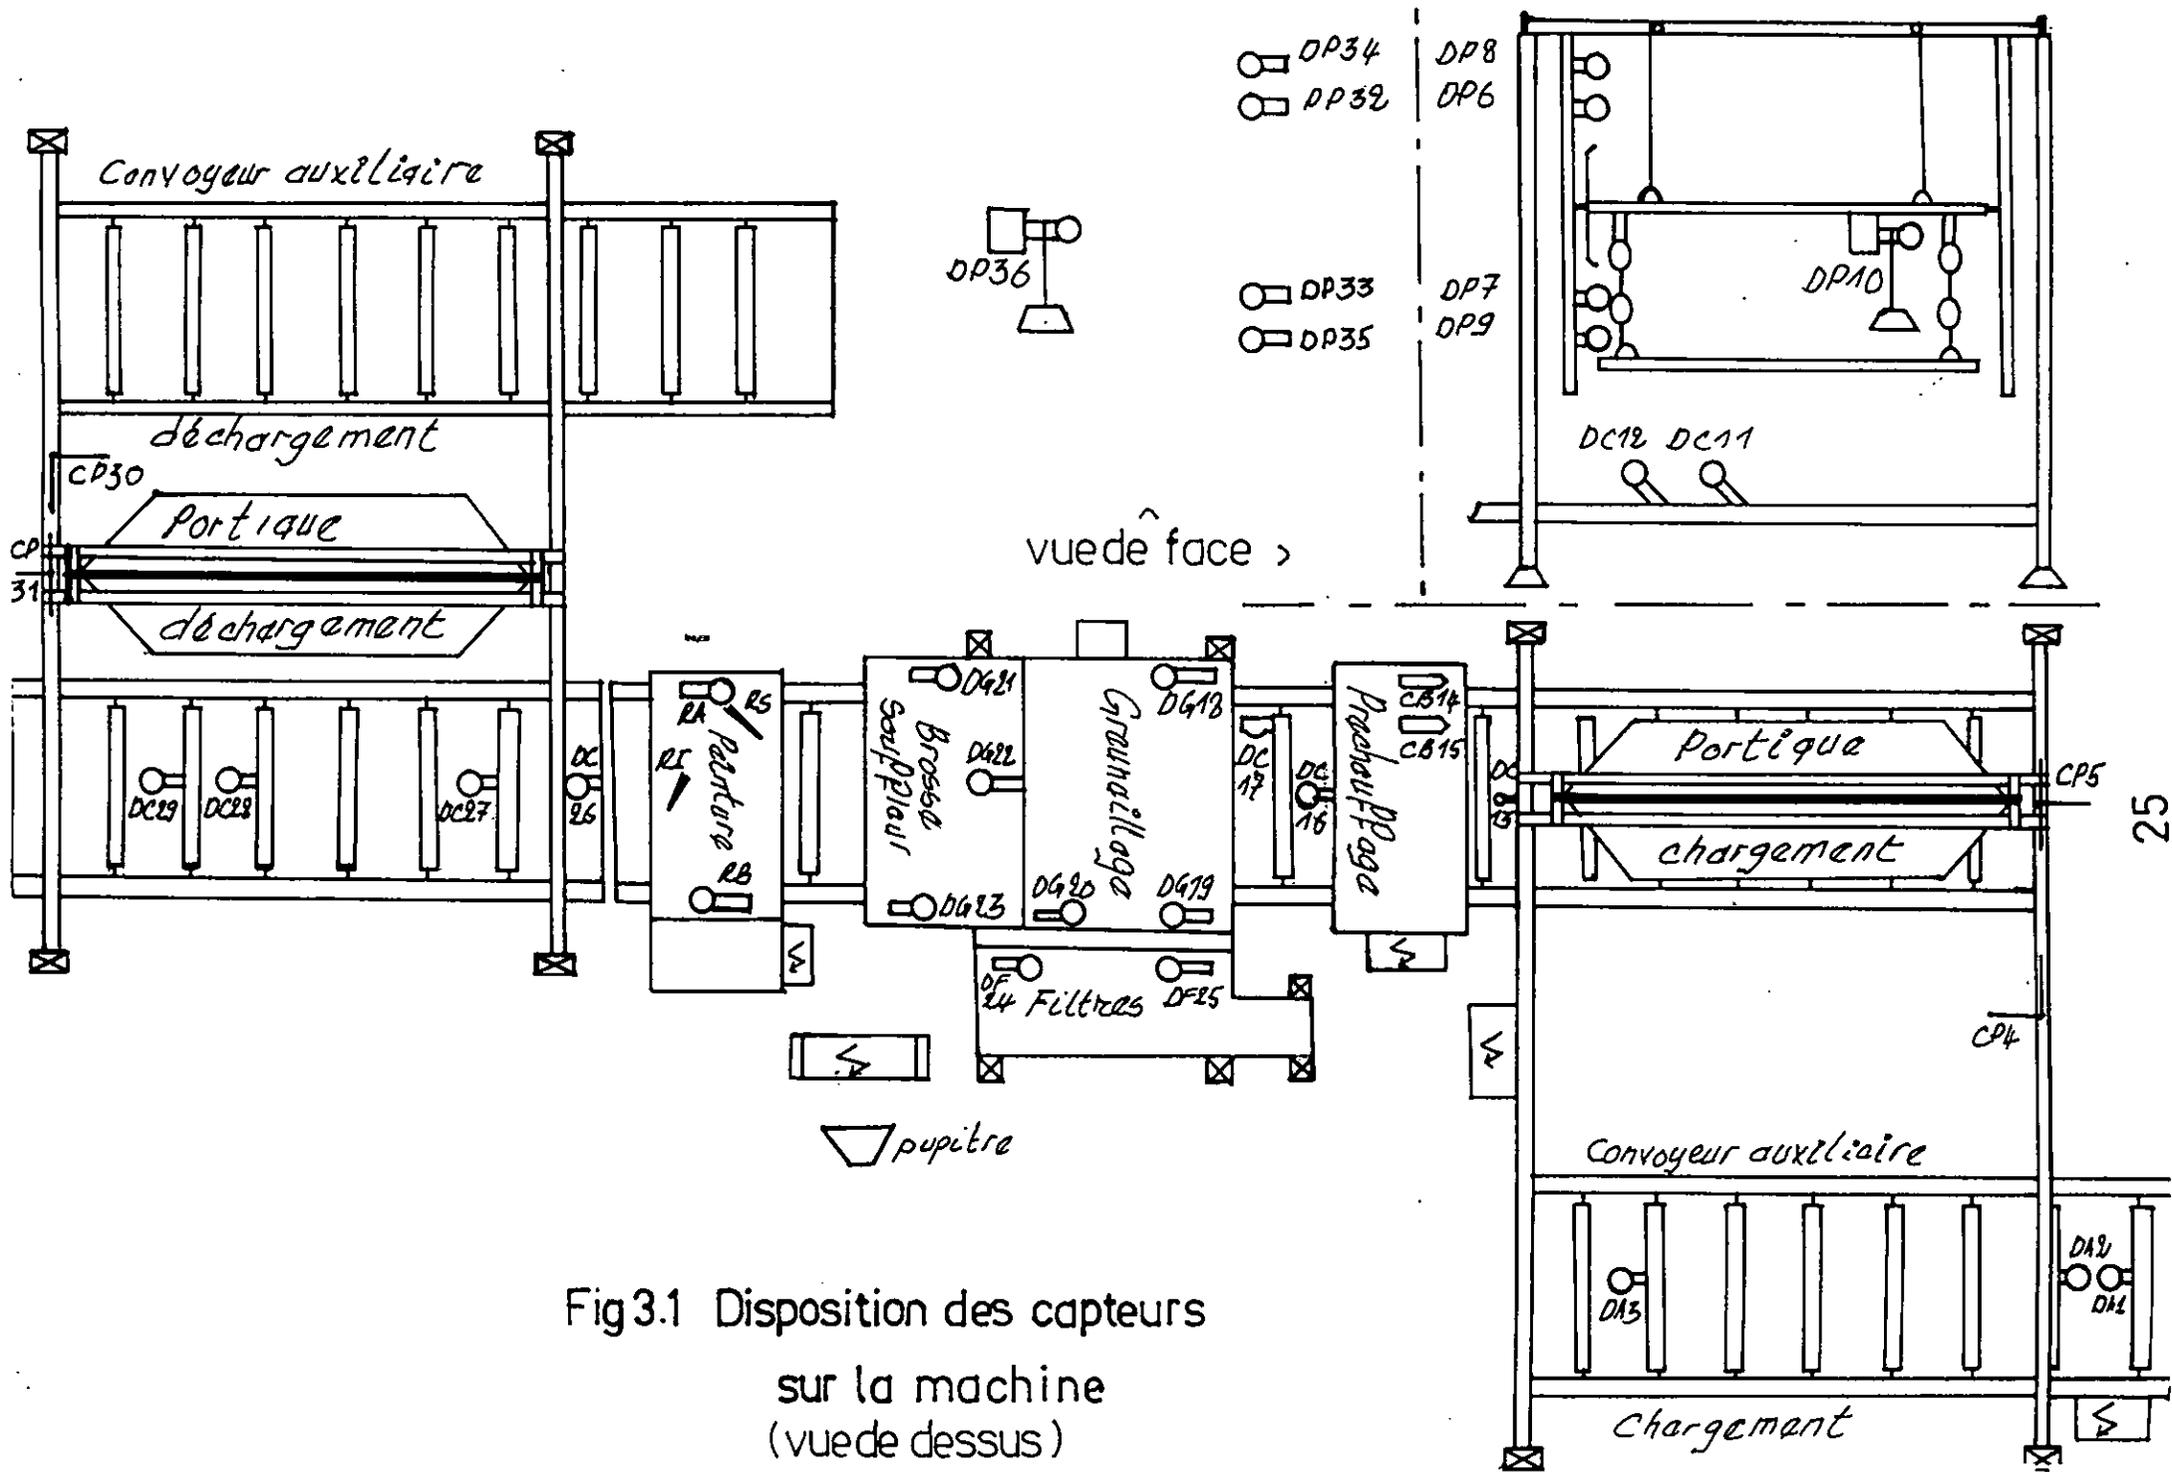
Disposition des capteurs sur la machine (vue de dessus)
